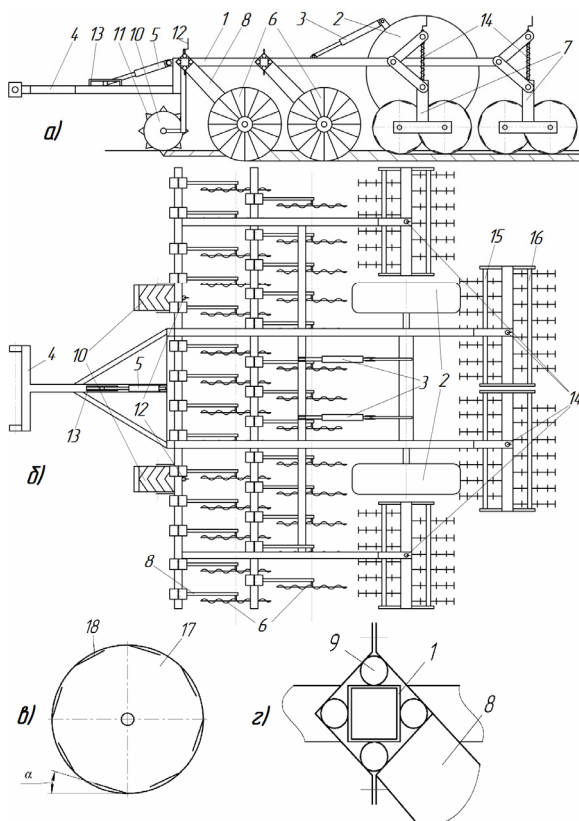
Схема агрегата для предпосевной обработки почвы в системе почвозащитного земледелия: а – агрегат, вид сбоку; б – агрегат, вид сверху; в – прикатывающий рабочий орган; г – защита стоек турбодисков на упругих элементах, 1 – рама; 2 – транспортные колеса; 3, 5 – гидроцилиндр; 4 – прицепное устройство; 6 – турбодиск; 7 – прикатывающие рабочие органы; 8 – стойка; 9 – упругий элемент; 10 – опорные колеса; 11 – рыхлитель; 12 – винтовой механизм; 13 – паз
